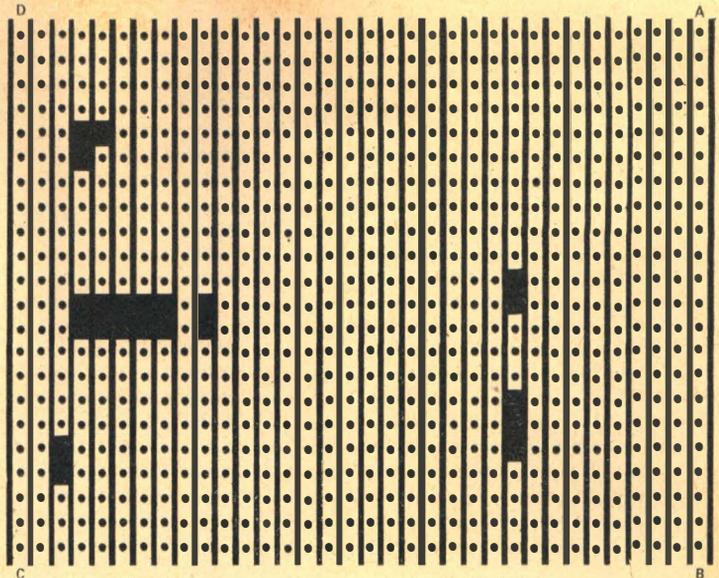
Plaqueta de circuito impresso universal utilizada para a montagem do analisador de cristais, mostrando os pontos onde foram interrompidos os filetes de cobre.
